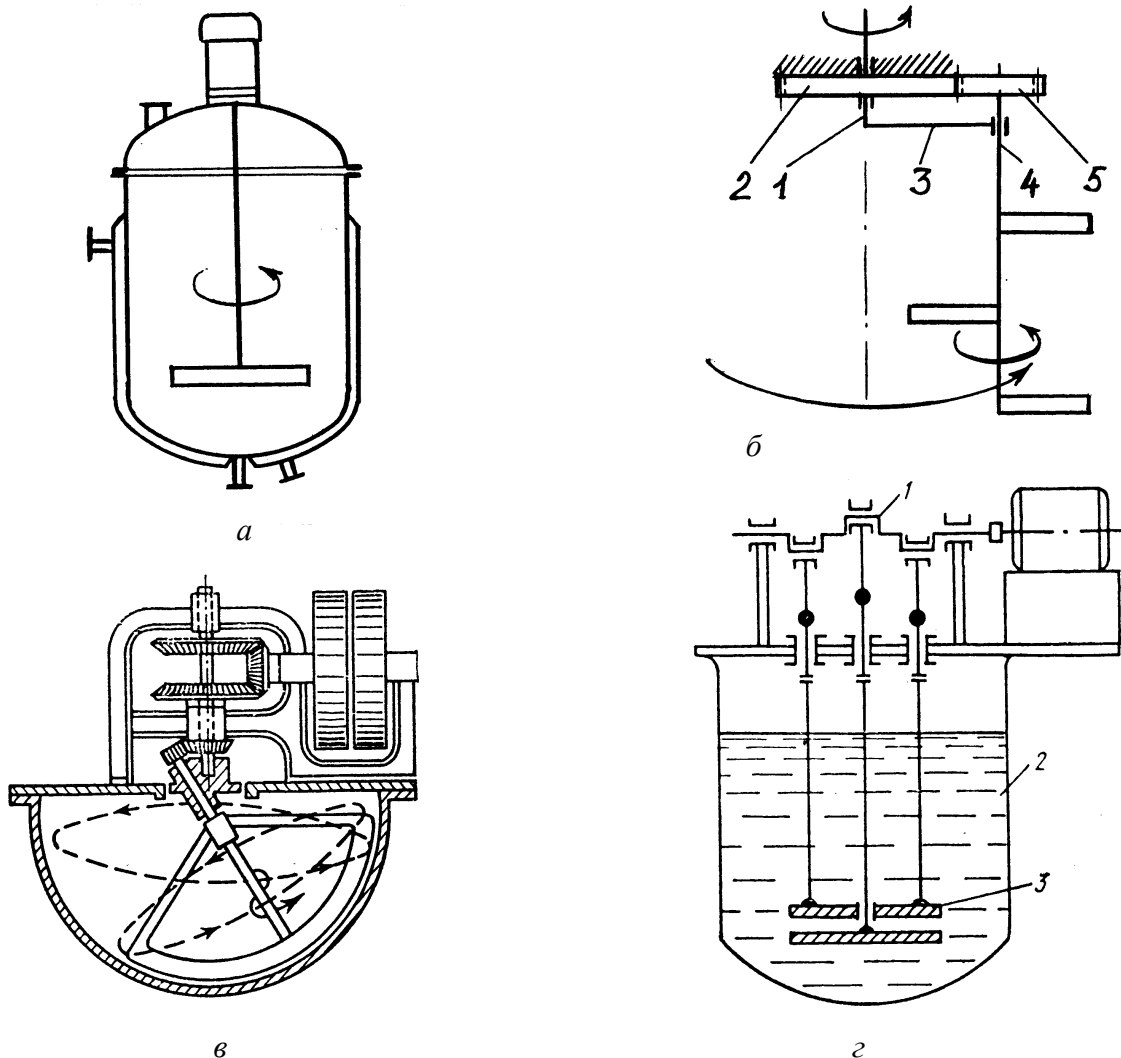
Схеми механічних перемішувальних пристроїв: *а* – роторного; *б* – планетарного: 1 – вал; 2 – нерухома шестірня; 3 – водило; 4 – вал мішалки; 5 – ведена шестірня; *в* – прецесійного; *г* – вібраційного: 1 – привід; 2 – корпус апарата; 3 – мішалка
